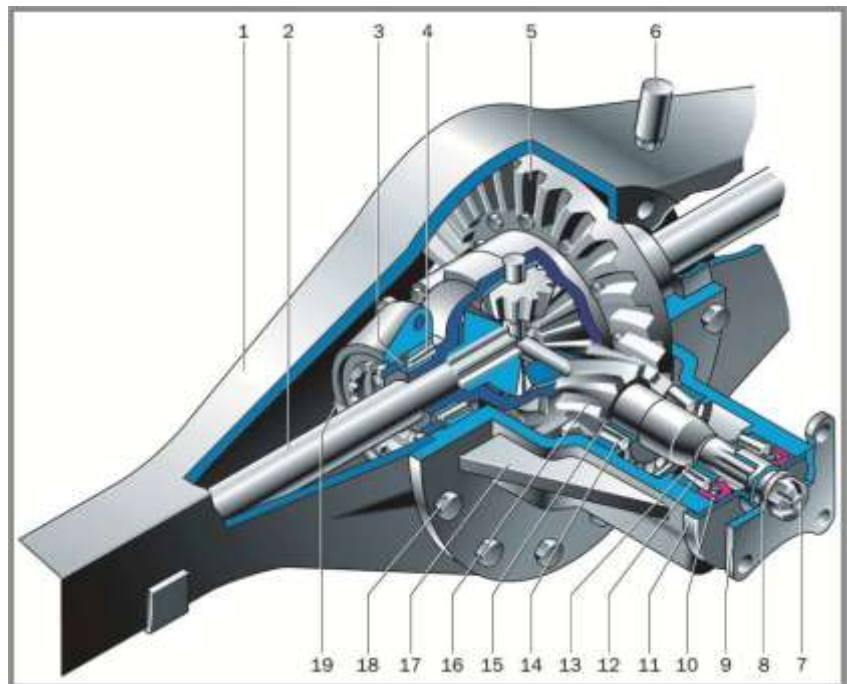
Гiпоїдна головна передача: 1 – картер заднього моста; 2 – пiввiсь; 3 – гайка пiдшипникiв диференцiала; 4 – пiдшипник диференцiала; 5 – ведена шестерня головної передачі; 6 – сапун; 7 – гайка; 8 – шайба; 9 – фланець провiдної шестернi; 10 – манжета; 11 – брудовiдбивач; 12, 14 – пiдшипники ведучої шестернi; 13 – кiльце розпору; 15 – регулювальне кiльце; 16 – ведуча шестерня; 17 – картер редуктора; 18 – болт; 19 – стопорна пластина
